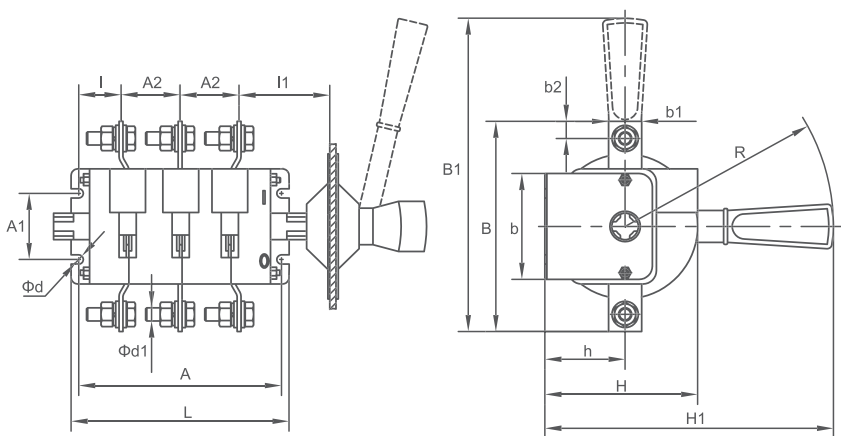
Выключатель-разъединитель универсальный трехполюсный на одно направление с д/г камерами, съемная левая/правая рукоятка
